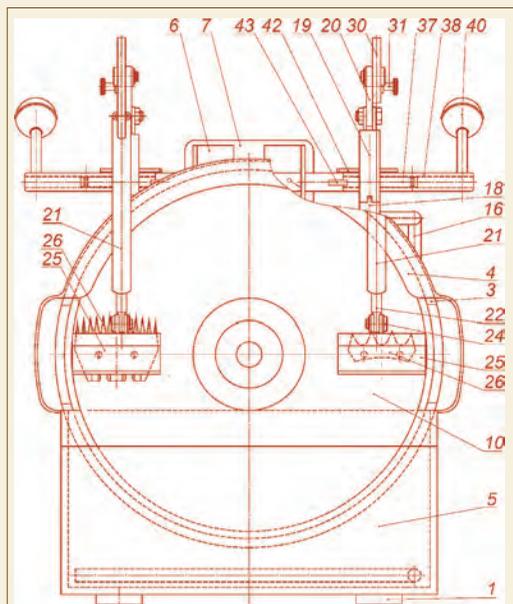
Полуавтомат для заточки режущих пар (вид спереди)
